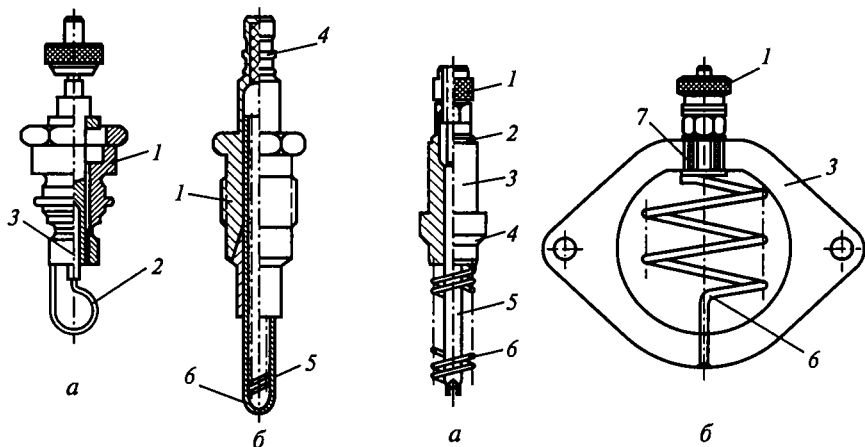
Конструктивные схемы свечей накаливания с открытым (а) и штифтовым (б) нагревательными элементами:
